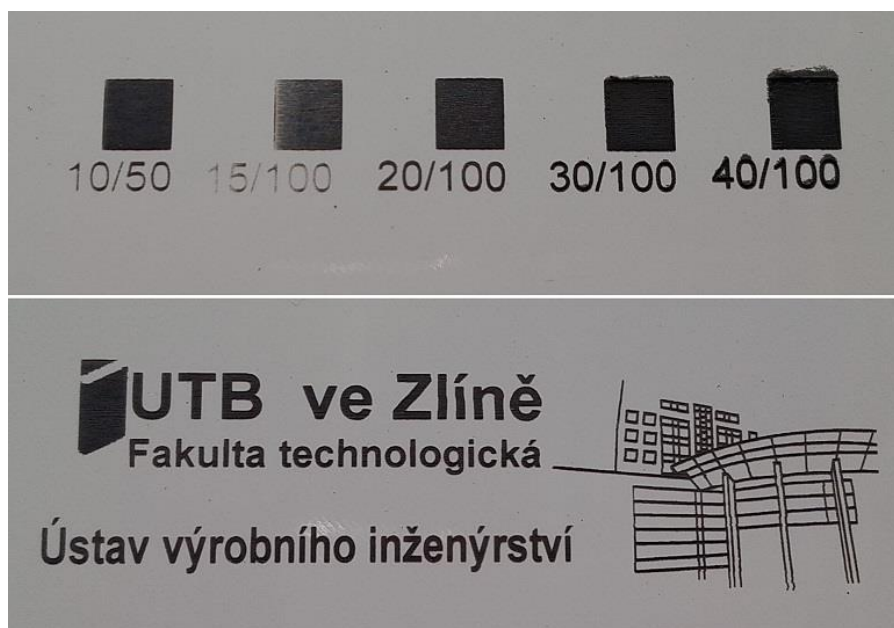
Experimentální obrábění vzorku produktu Laserables Reverse - stříbrný
